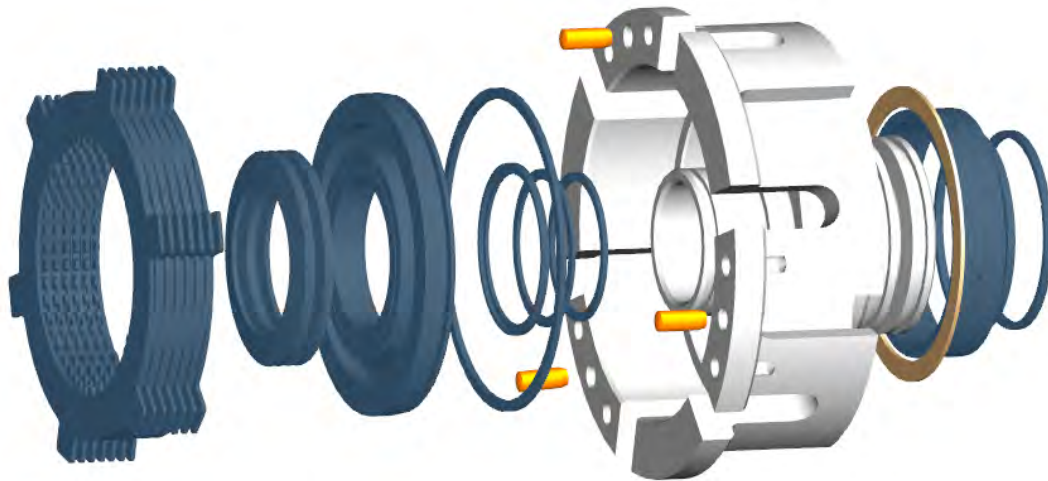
"Explosionado del embrague inferior del eje de entrada"
